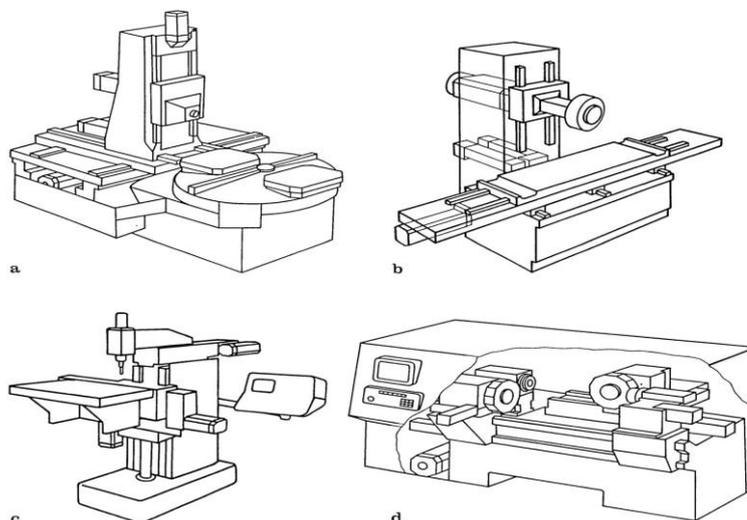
Beispiel: eine Werkzeugmaschine (Wikipedia)
